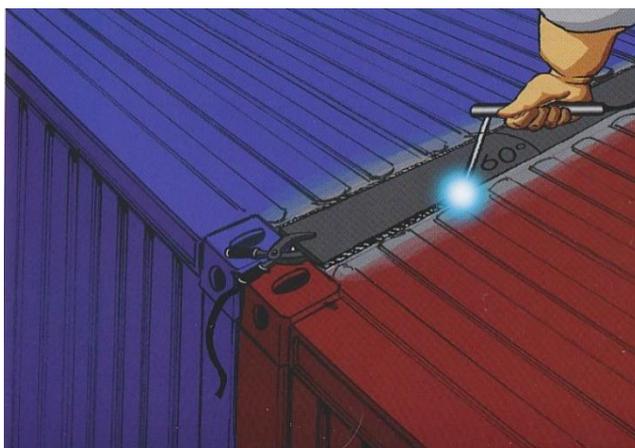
Technique de soudure pour containers (FOSSOUX et CHEVRIOT, 2011)
